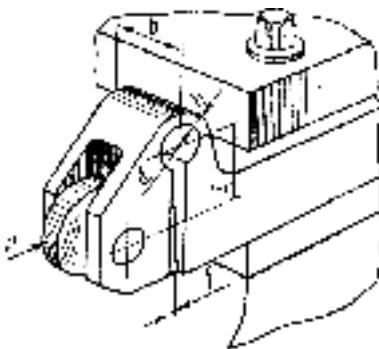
Пристрій для обкатування деталей роликами з пружівним корпусом:
